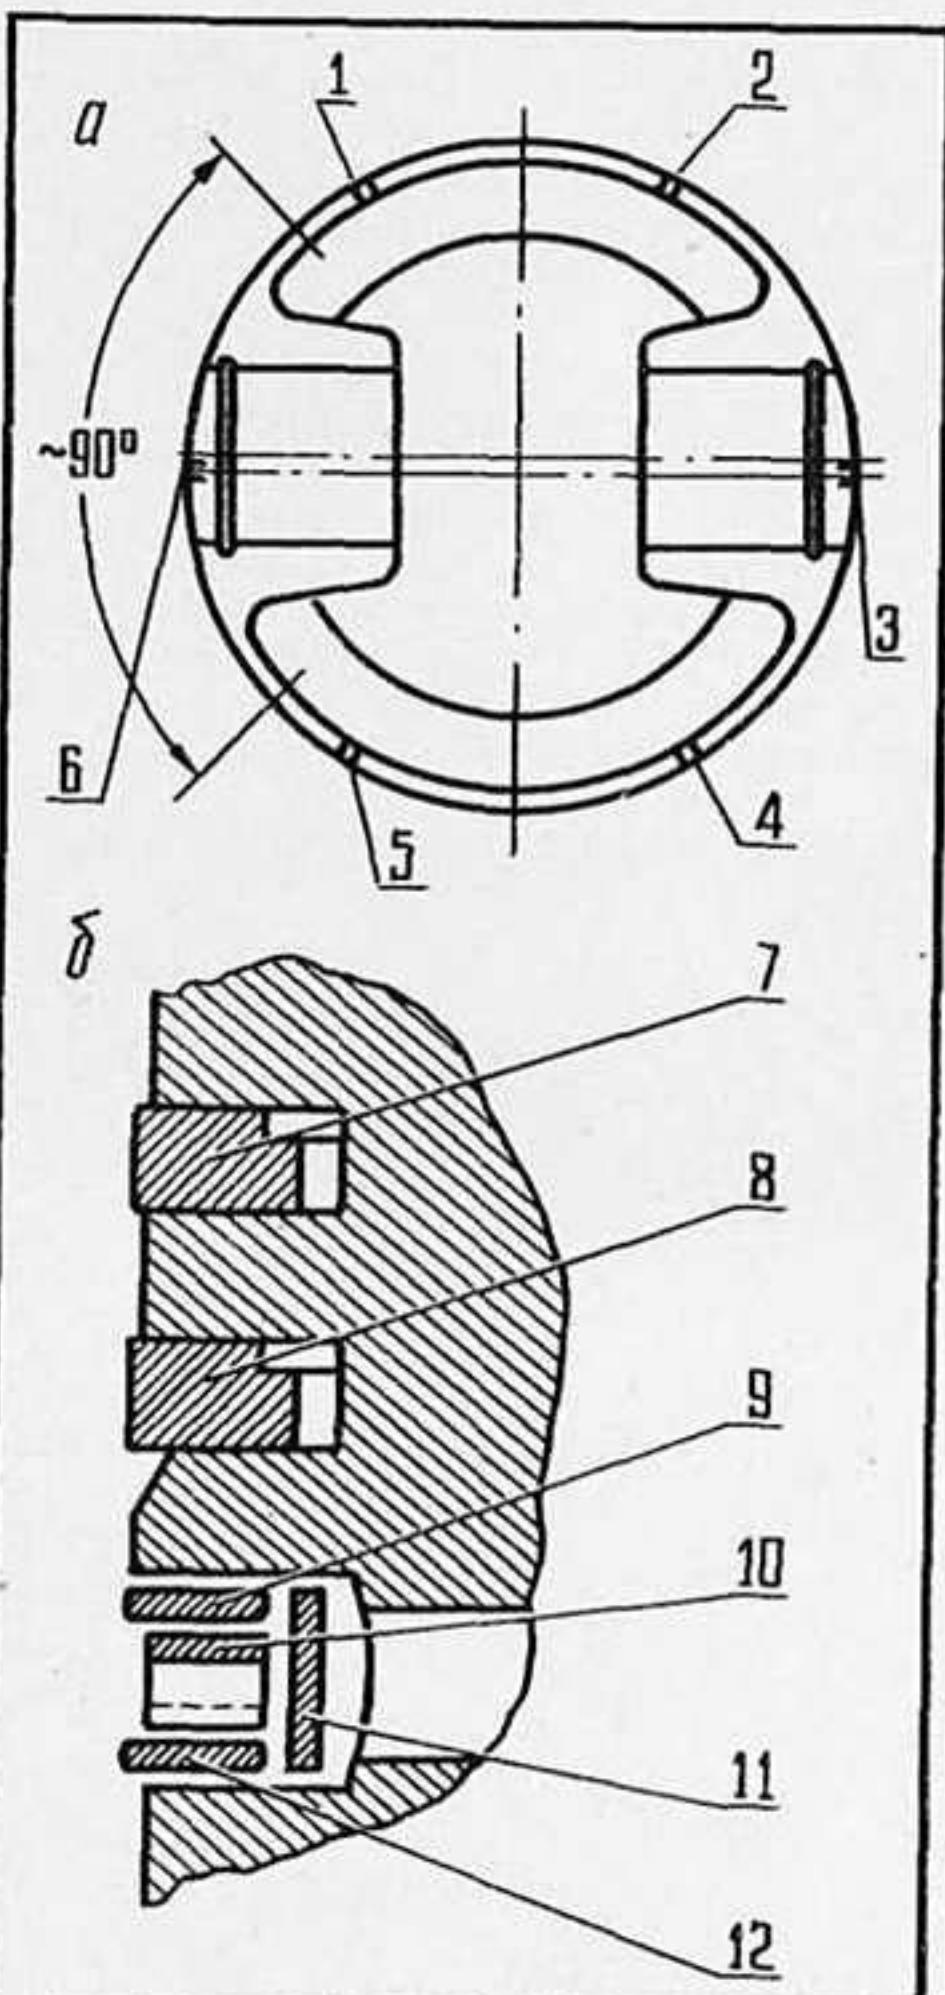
Схема установки поршневых колец: а — расположение замков; б — установка поршневых колец; 1 — замок верхнего компрессионного кольца; 2 — замок верхнего диска маслосъемного кольца; 3 — замок осевого расширителя; 4 — замок нижнего компрессионного кольца; 5 — замок нижнего диска маслосъемного кольца; 6 — замок радиального расширителя; 7 — верхнее компрессионное кольцо (хромированное); 8 — нижнее компрессионное кольцо (луженое); 9 — верхний диск маслосъемного кольца; 10 — осевой расширитель; 11 — радиальный расширитель; 12 — нижний диск маслосъемного кольца; на участке, обозначенном углом 90°, с обеих сторон не должно быть замков.
